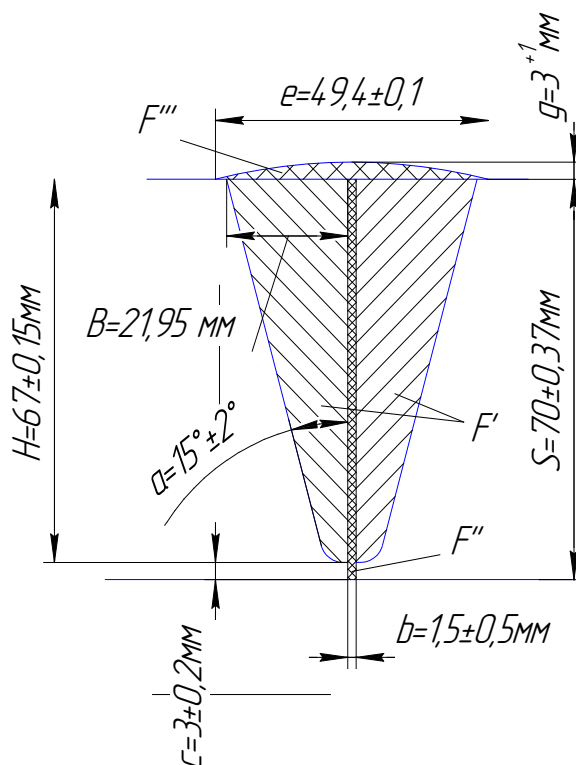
Схема общей площади поперечного сечения сварного шва
